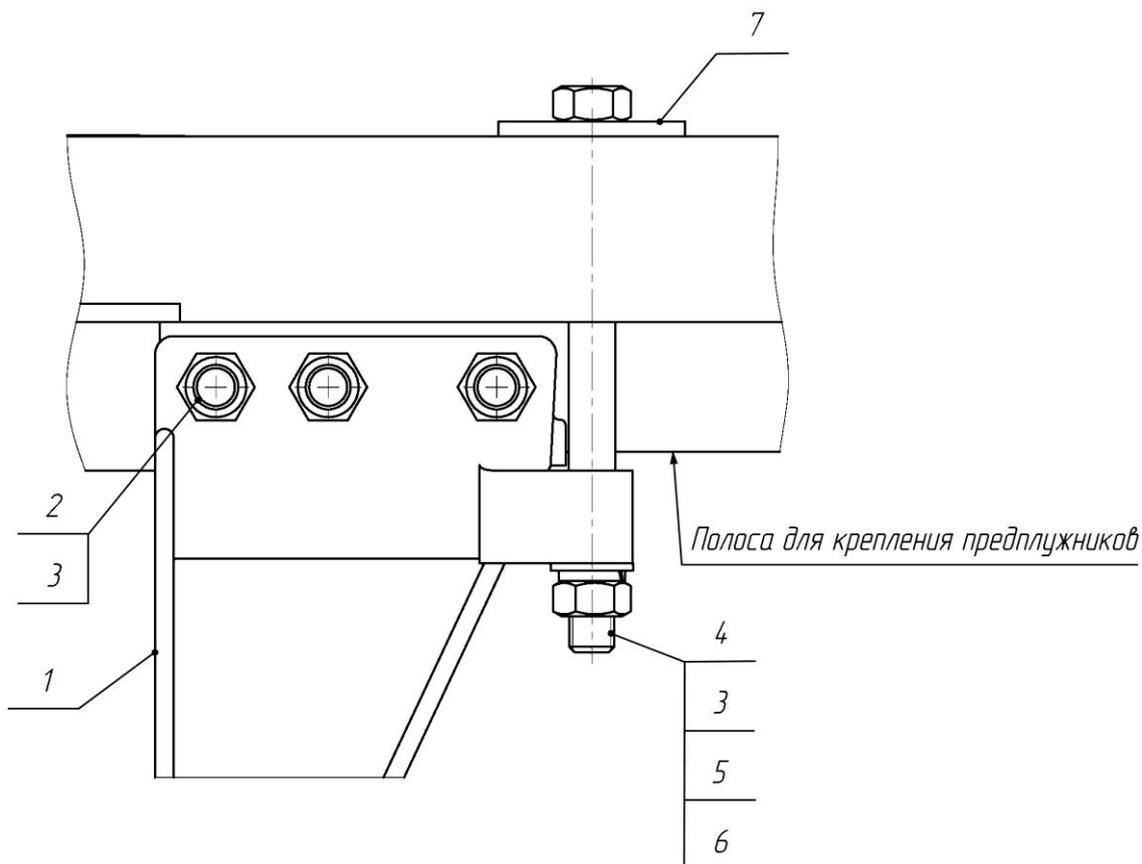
а Крепление корпуса рабочего к раме плуга ПЛНУ-5-35/ПЛНУ-5-35П
